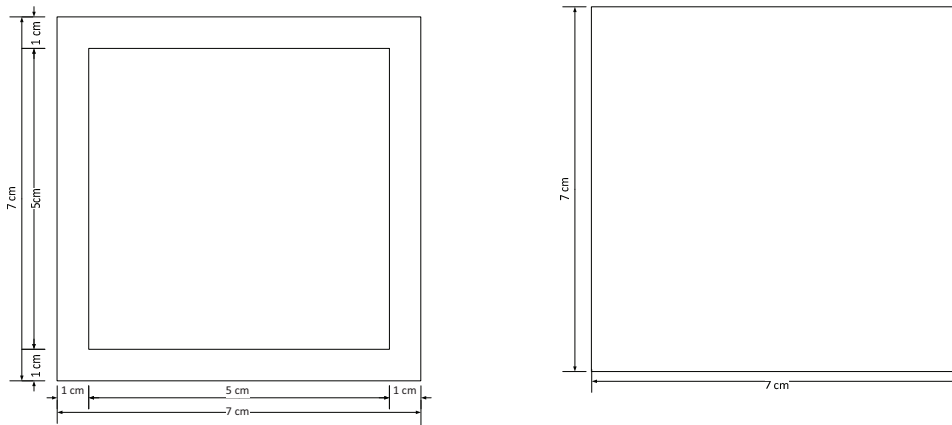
Molde tipo flash utilizado para la elaboración de probetas por moldeo a compresión
